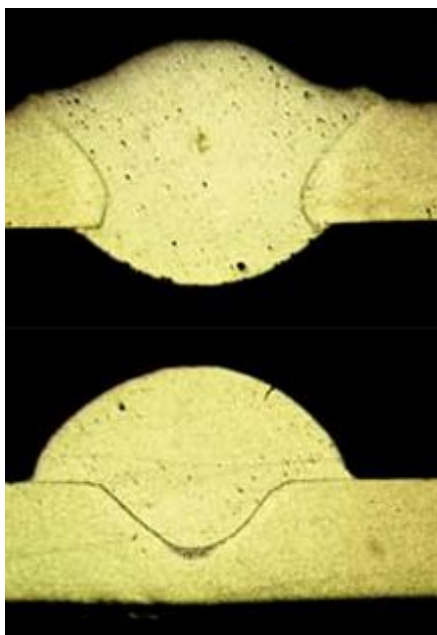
Detail svaru plechů tloušťky 0,98 mm
